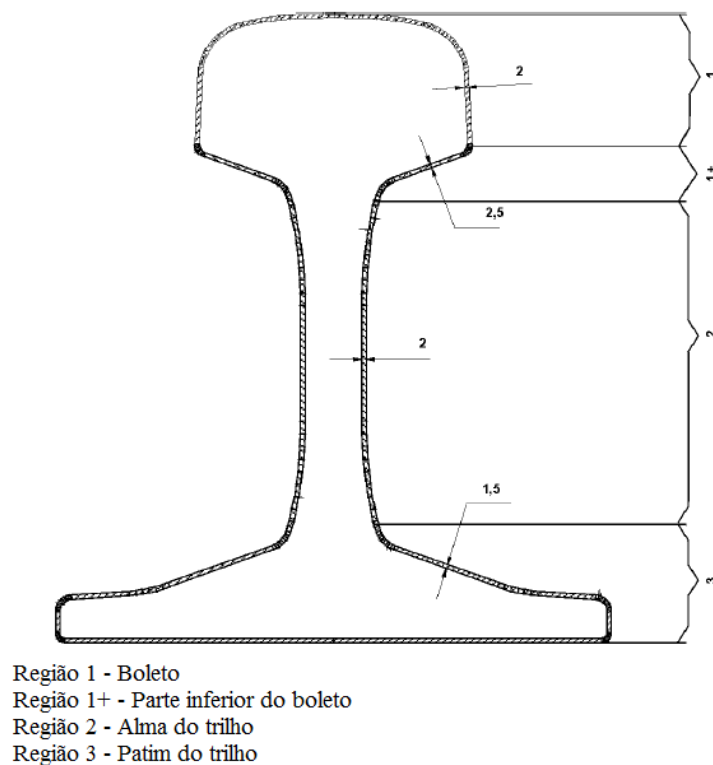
Requisitos de acabamento superficial na região de junta soldada de trilho por centelhamento após a remoção de rebarba a quente ao final da soldagem por centelhamento elétrico. Dimensões em mm, valores máximos de altura de rebarba permitida. Adaptado de EN 14587-1 (2005).
